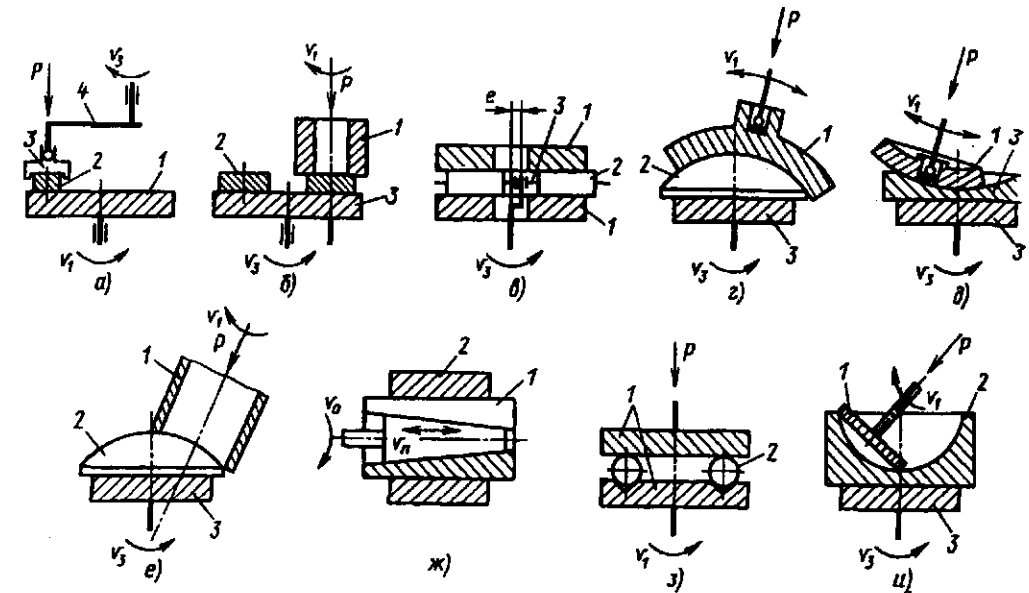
Основные схемы доводки плоских (а, б), цилиндрических (в, ж) и сферических (з – е, з, и) поверхностей: 1 – притир; 2 – деталь; 3 – устройство для установки детали; v_1 – скорость притира; v_0 – скорость заготовки; v_0 – окружная скорость; v_n – скорость возвратно-поступательного движения; P – сила прижима
